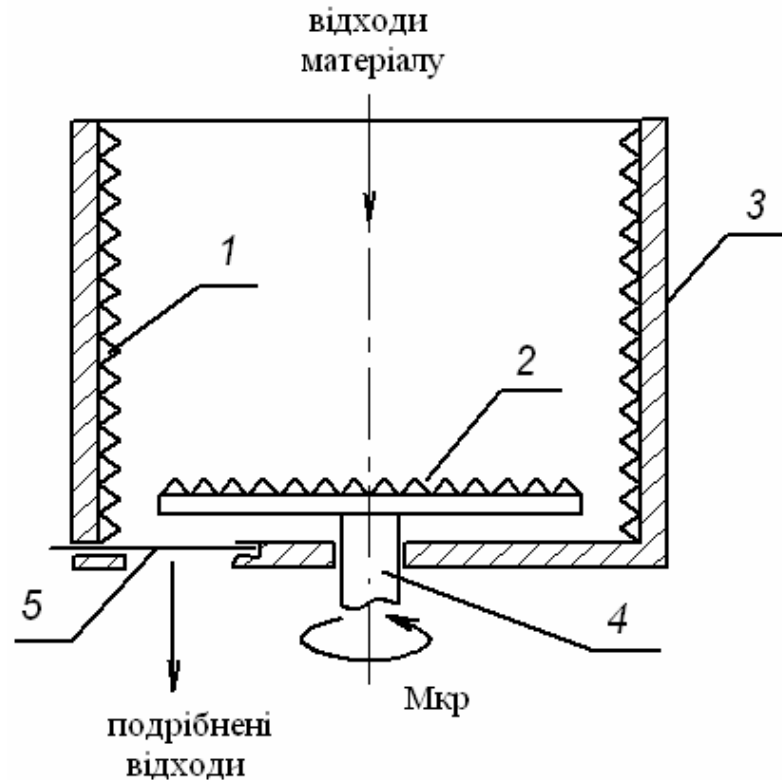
Відцентровий подрібнювач: 1 – рифлі, розташовані на корпусі; 2 – рифлі, розташовані на роторі; 3 – корпус; 4 – вал; 5 – заслінка
